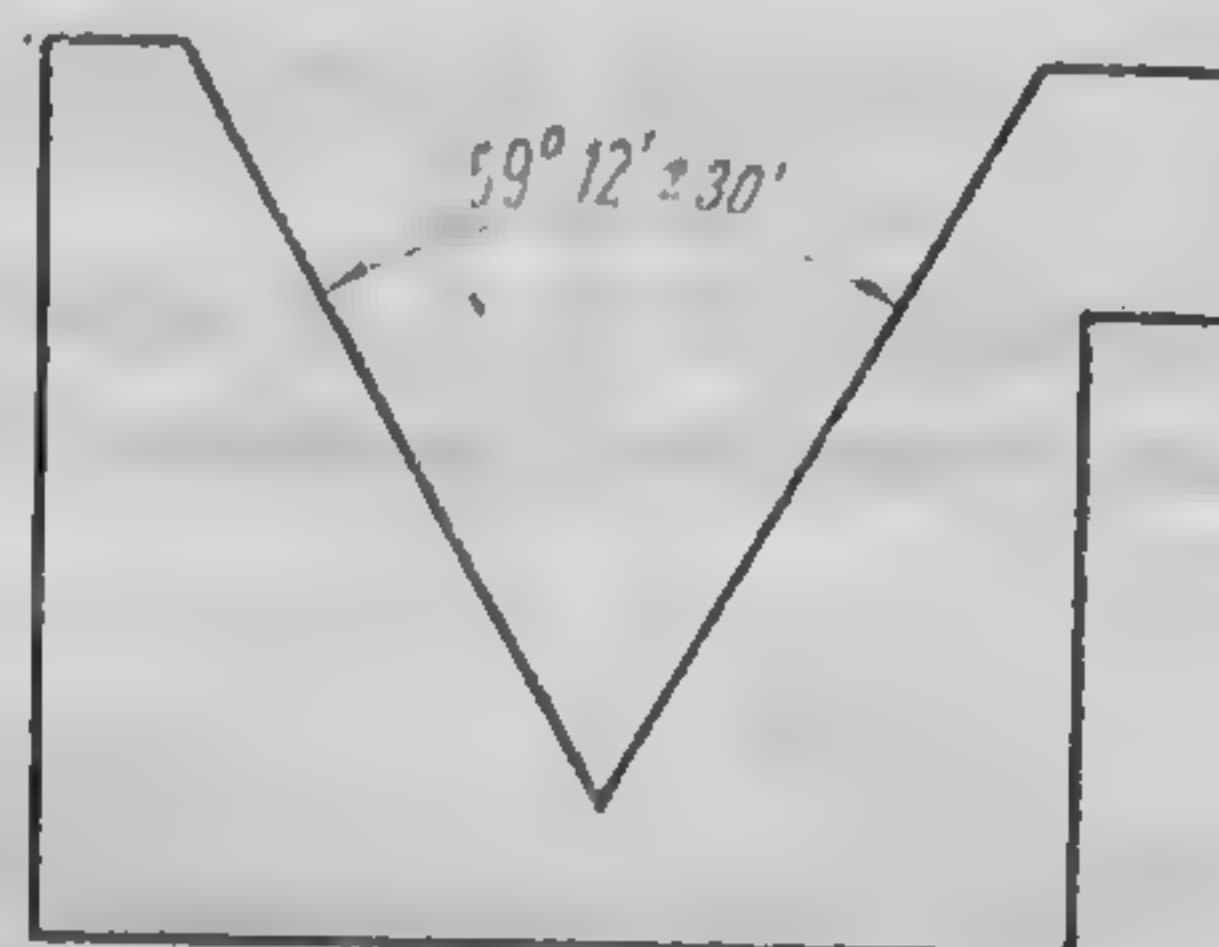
Înscriserea toleranței la dimensiuni unghiulare în cazul abaterilor limită simetrice față de dimensiunea nominală.
